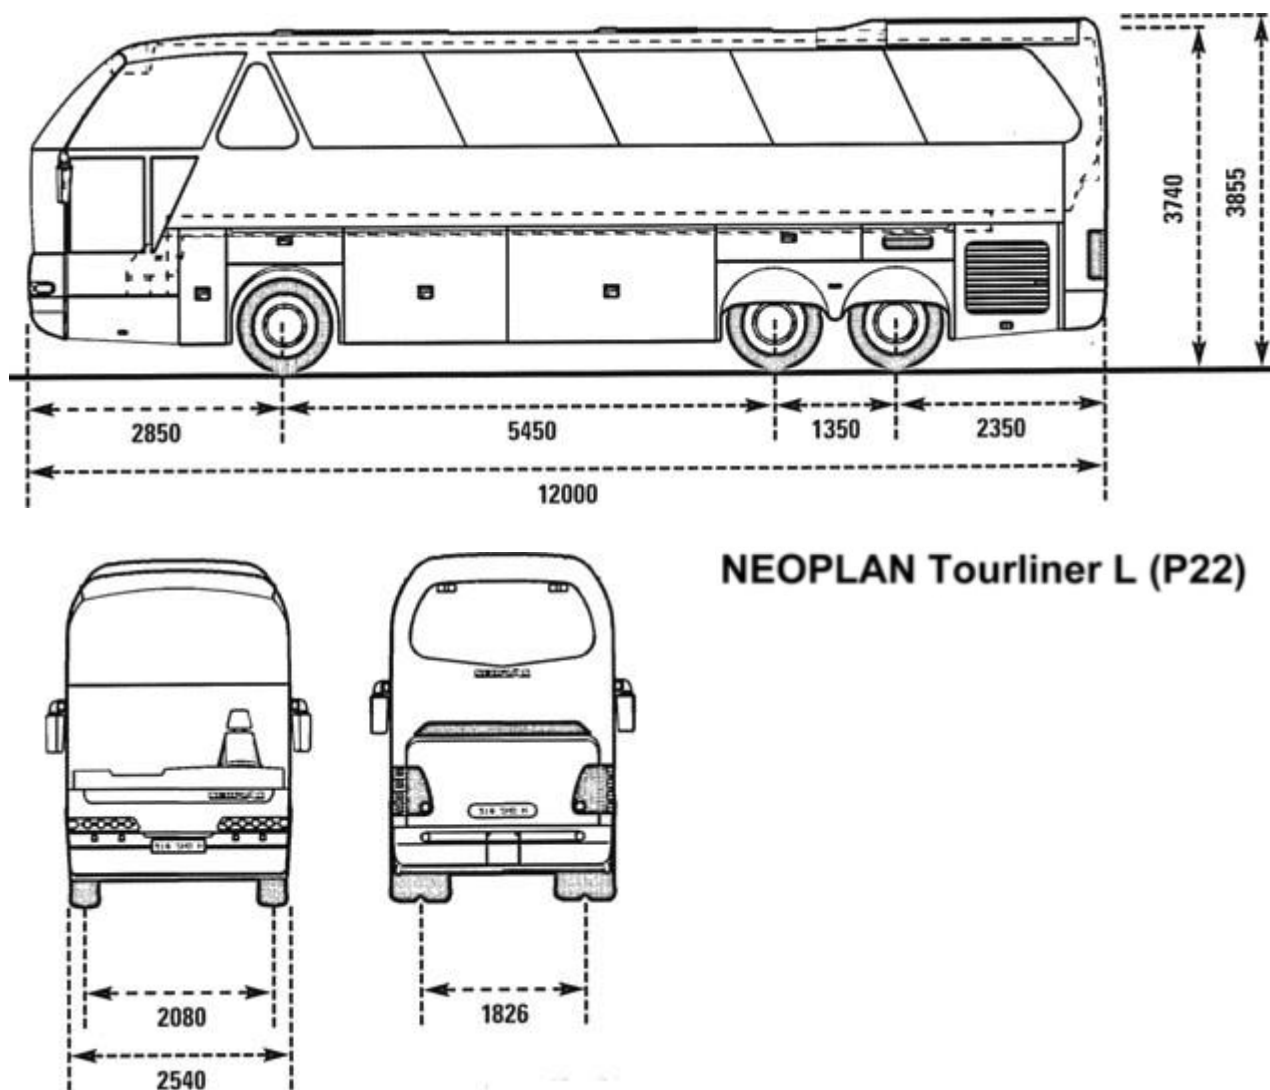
Габаритне креслення автобуса NEOPLAN Tourliner L (P22)
